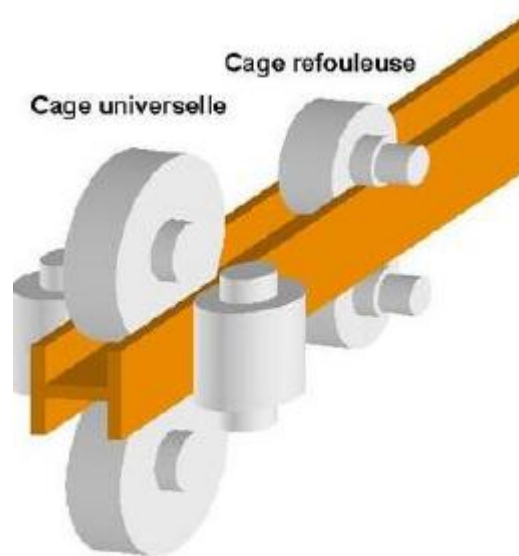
cage universelle et cage refouleuse : laminage des poutrelles
